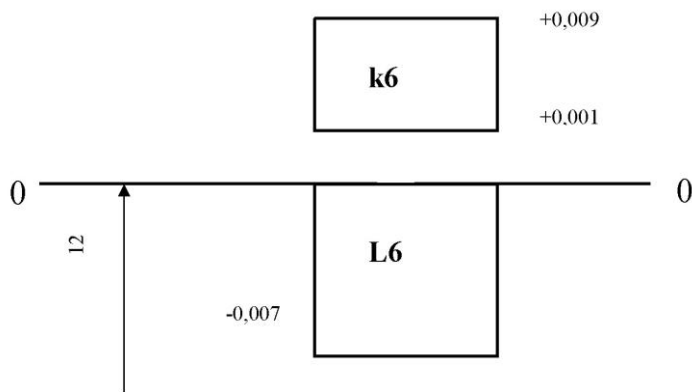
Схема посадки внутреннего кольца подшипника на вал
